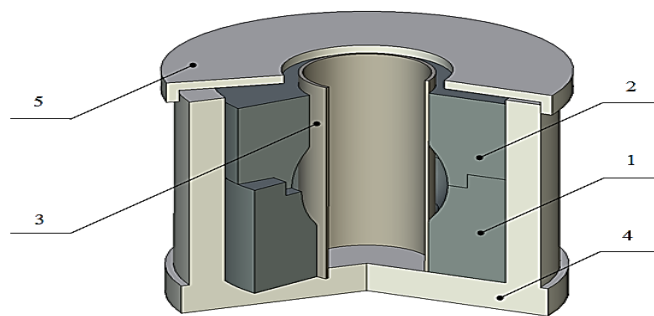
Штамп для раздачи трубчатой заготовки
